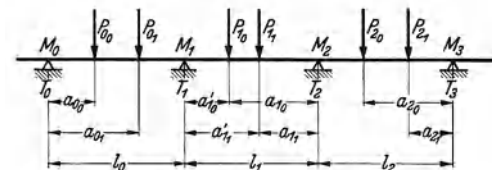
Ermittlung der Lagermomente und Lagerdrücke an einer 6-Zylinder-Welle mit 4 Lagern.
